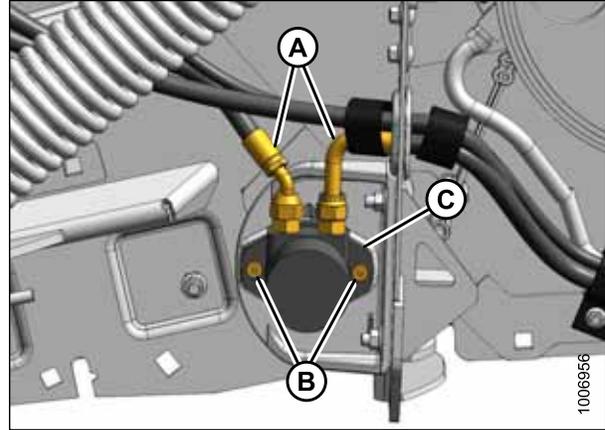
Motor hidráulico trasero; lado izquierdo
